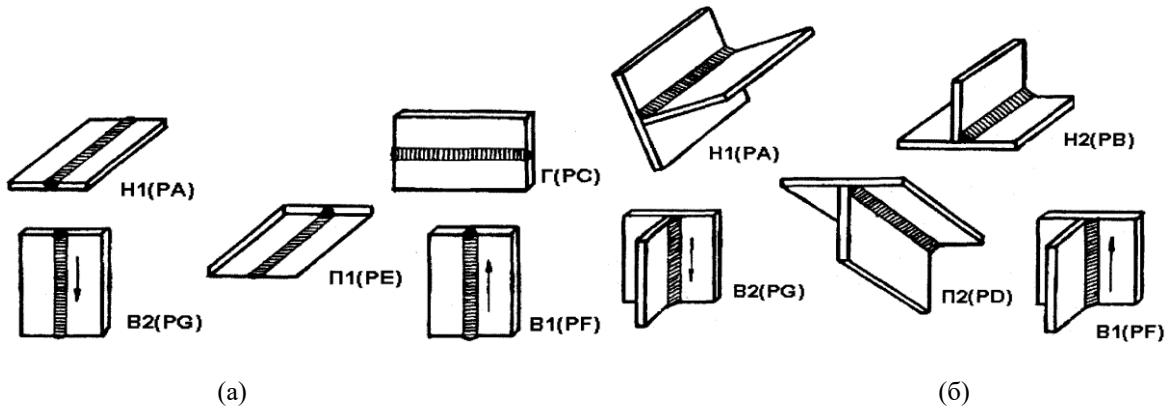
Положения при сварке стыковых (а) и тавровых (б) соединений листов:
